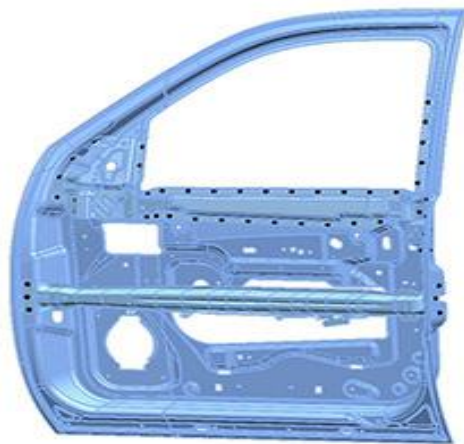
Herramienta de diseño de soldadura NX
